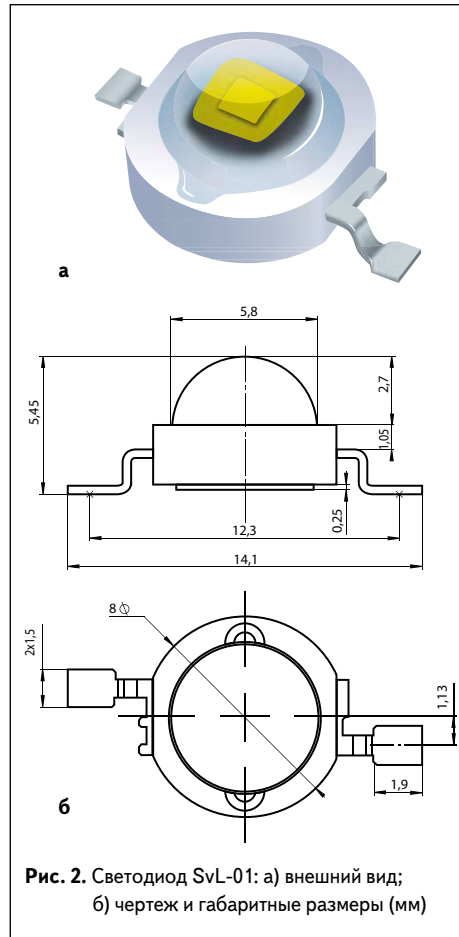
Светодиод SvL-01: а) внешний вид; б) чертеж и габаритные размеры (мм)
